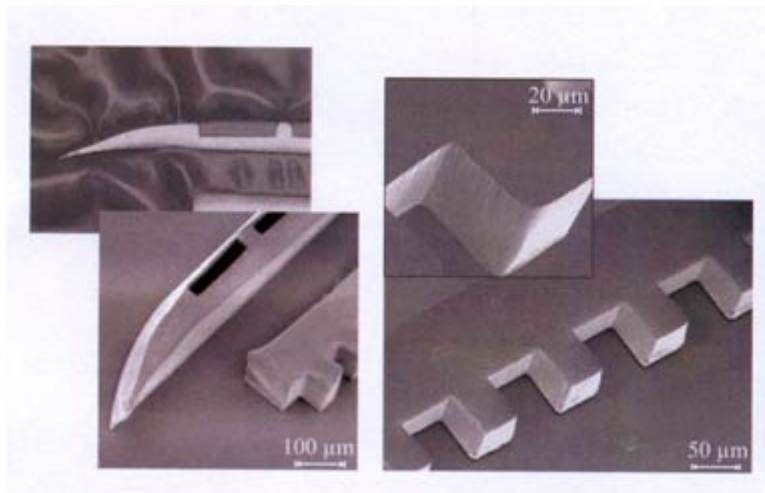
Links: Forminstabilität von AZ 9260 in heißen Galvaniken im Gegensatz zu galvanisch abgedruckten Strukturen in formstabilen CAR 44 Galvanoformen (rechts)
